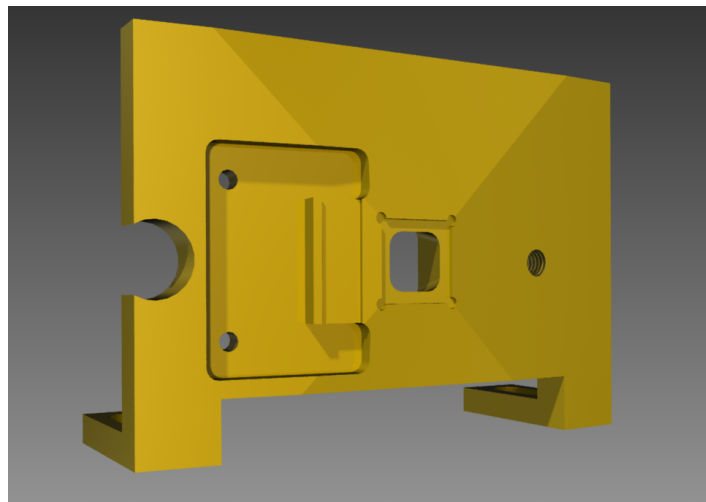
Technische Darstellung des Halters für das Bolometer. Die Front ist mit einem Winkel von 5° angeschrägt und hat Aussparungen verschiedener Tiefe für SQUIDs und Platine. Mittig befindet sich eine nach hinten öffnende Durchführung mit einem Absatz zur Aufnahme des Bolometers.
